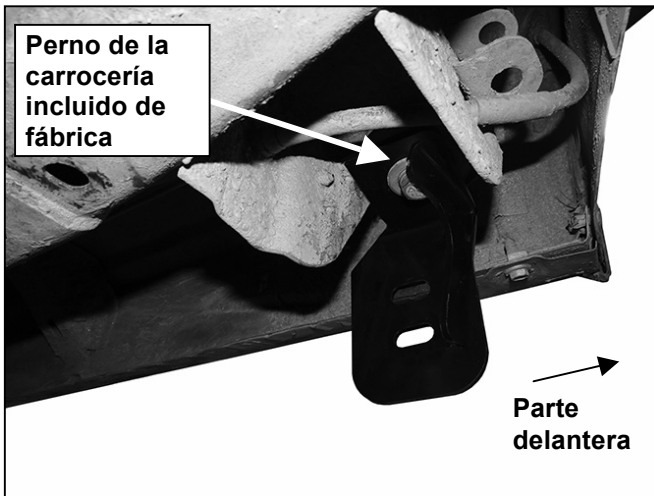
A) Soporte frontal izquierdo/del lado del conductor
